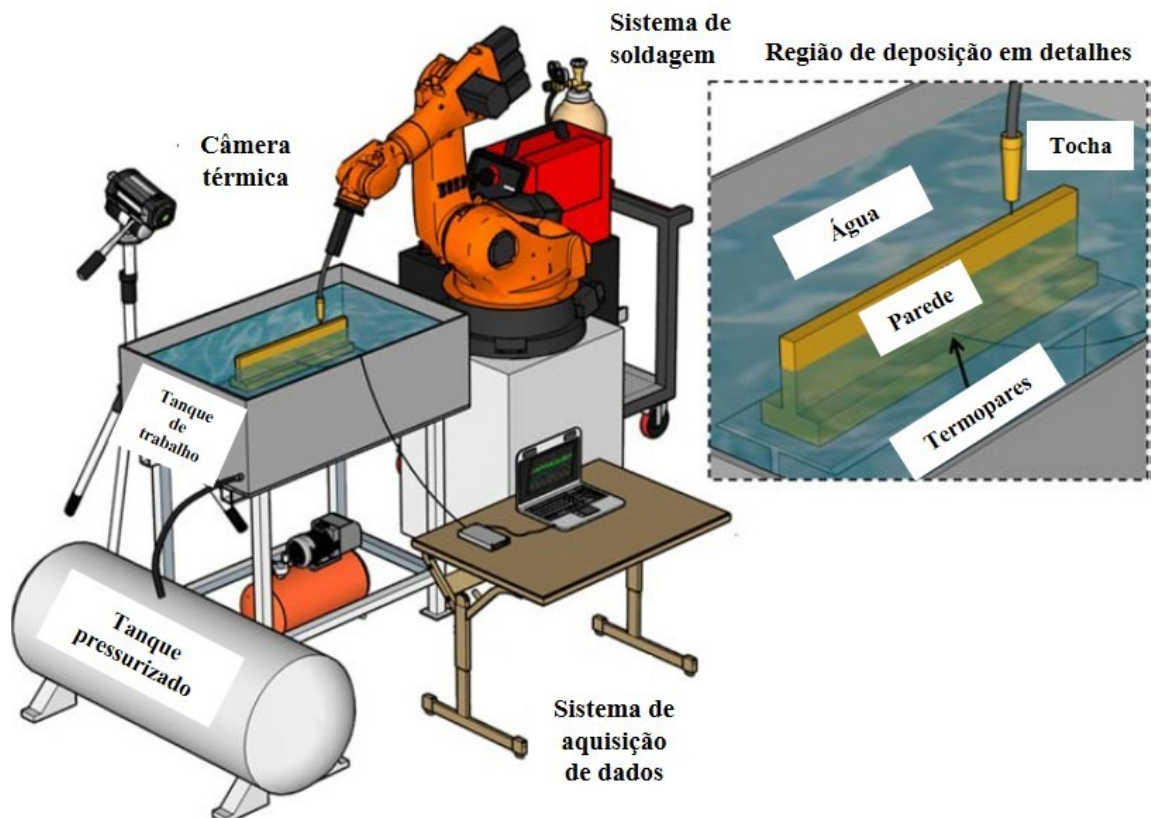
Montagem experimental com o robô industrial e o tanque de água (adaptada pelo autor)
